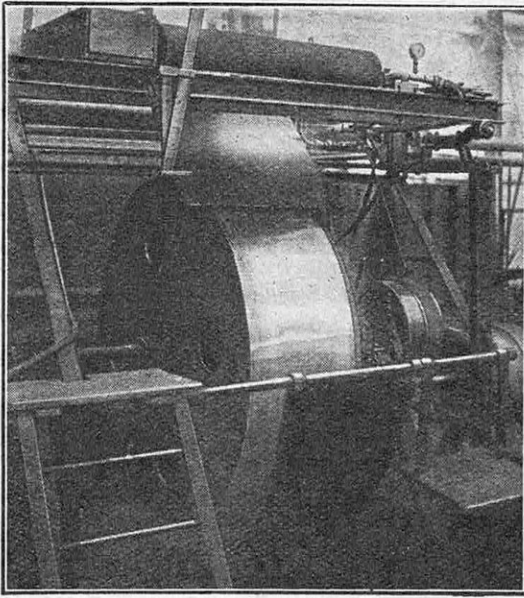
FABRICATION DE LA SOIE DE VERRE
